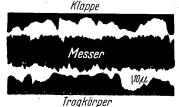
1. Messerbefestigungen zusammengesetzter Holzfräswerkzeuge.
